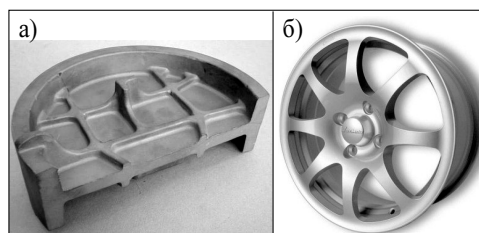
Детали, полученные объёмной штамповкой: а) — титановый корпус; б) — автомобильный диск
